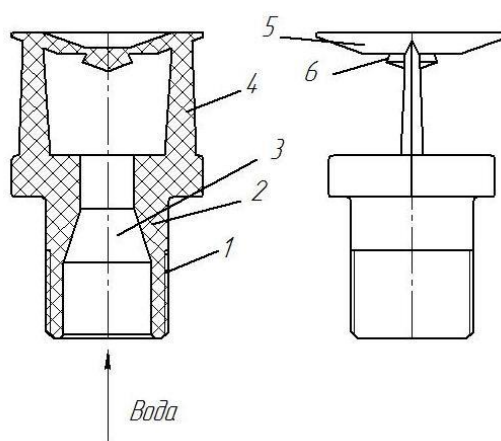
Предлагаемая дождевальная дефлекторная насадка: 1 – резьба; 2 – корпус; 3 – сопло; 4 – ножка дефлектора; 5 – дефлектор; 6 – канавка.
